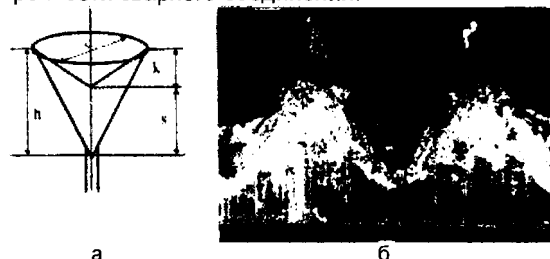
Импульсный лазерный сварной шов: а - схема сварной точки на стыке деталей (h - глубина проплавления, k - глубина кратера, d - диаметр кратера, s - глубина сплавления), б - продольный разрез шва
